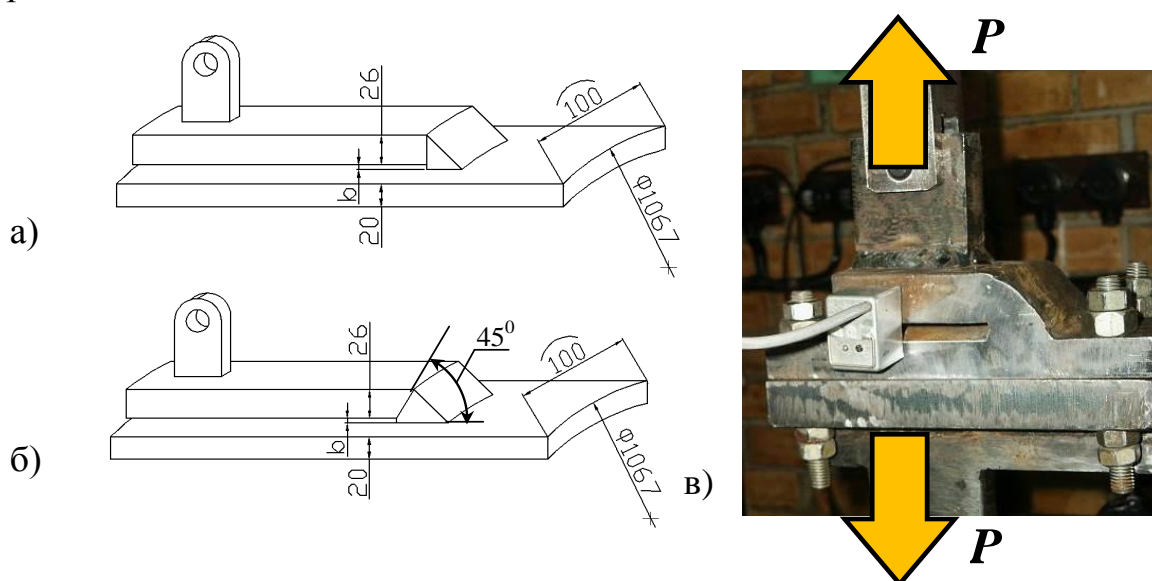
Лабораторные образцы для изучения влияния технологии сборки и сварки на ресурс сварного соединения: а) образец без обратного скоса кромок; б) образец с обратным скосом кромки; в) схема приложения нагрузки к образцу
